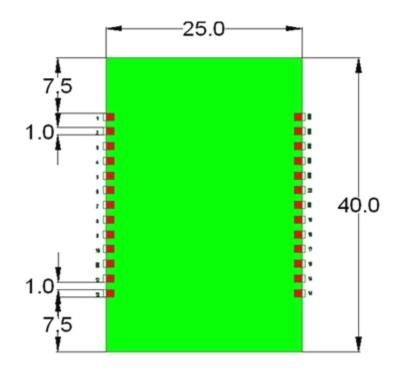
USR-WIFI232-Ca/Cb 模块尺寸图
